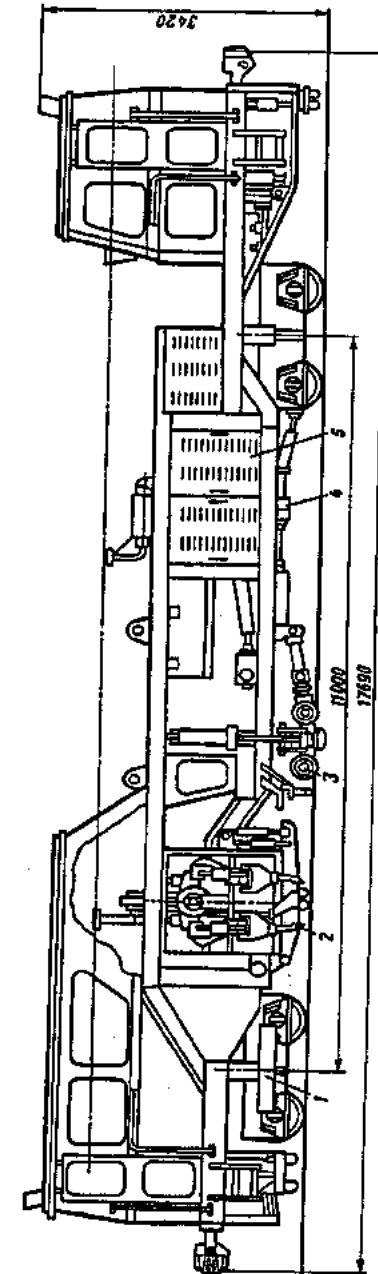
Выправочно-подбивочно-рыхловочная машина ВПРС: 1 — уплотнитель балласта; 2 — подбивочный блок; 3 — механизм подсыла и сдвиги пути; 4 — силовая передача; 5 — энергетическая установка
